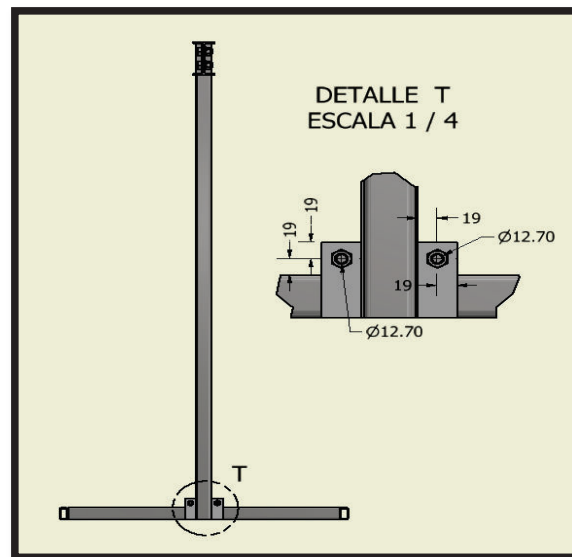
Conexión columna posterior-soporte del contrapeso.
